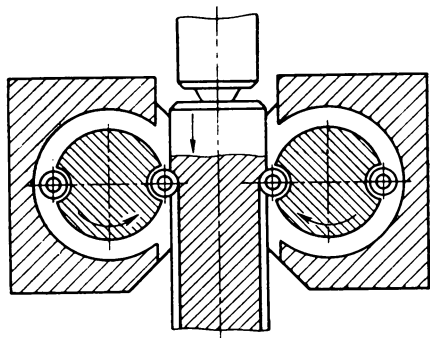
Схема ударного накатывания зубьев вала вращающимся роликовыми головками
